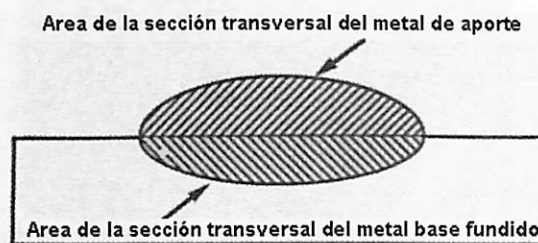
Ilustración de la dilución en un cordón de soldadura. (ref. 5)
